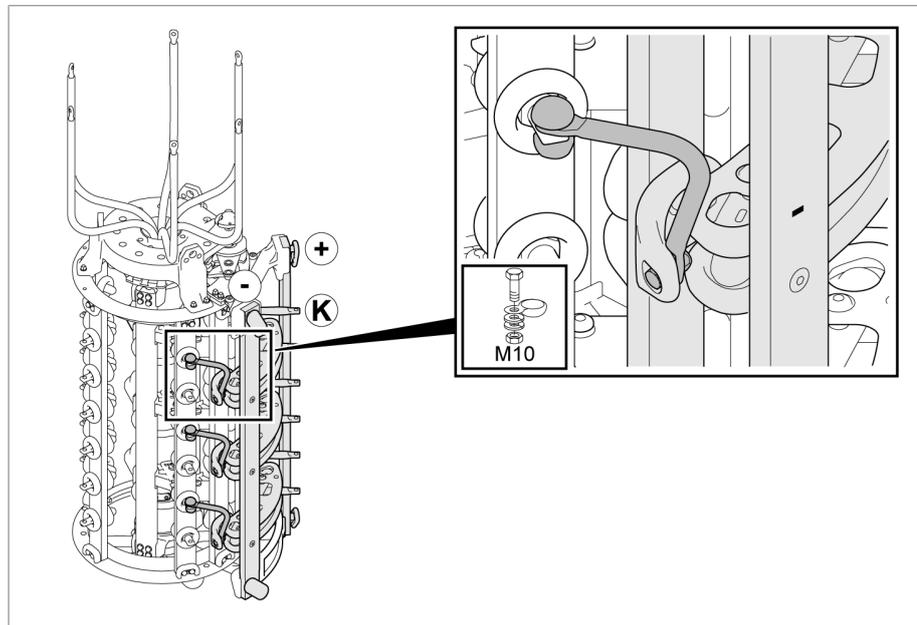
Присоединительные контакты преобразователя при исполнении преобразователя с реверсом
